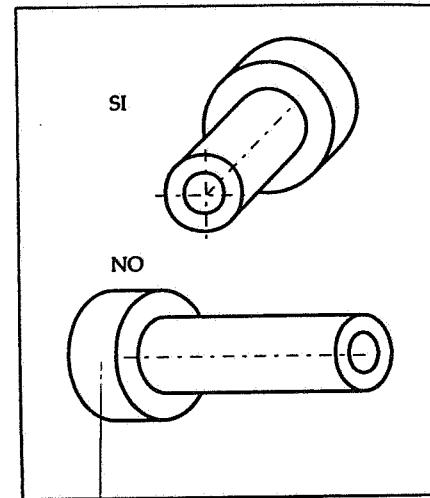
Disposizione di pezzi nell'assonometria cavalliera.
